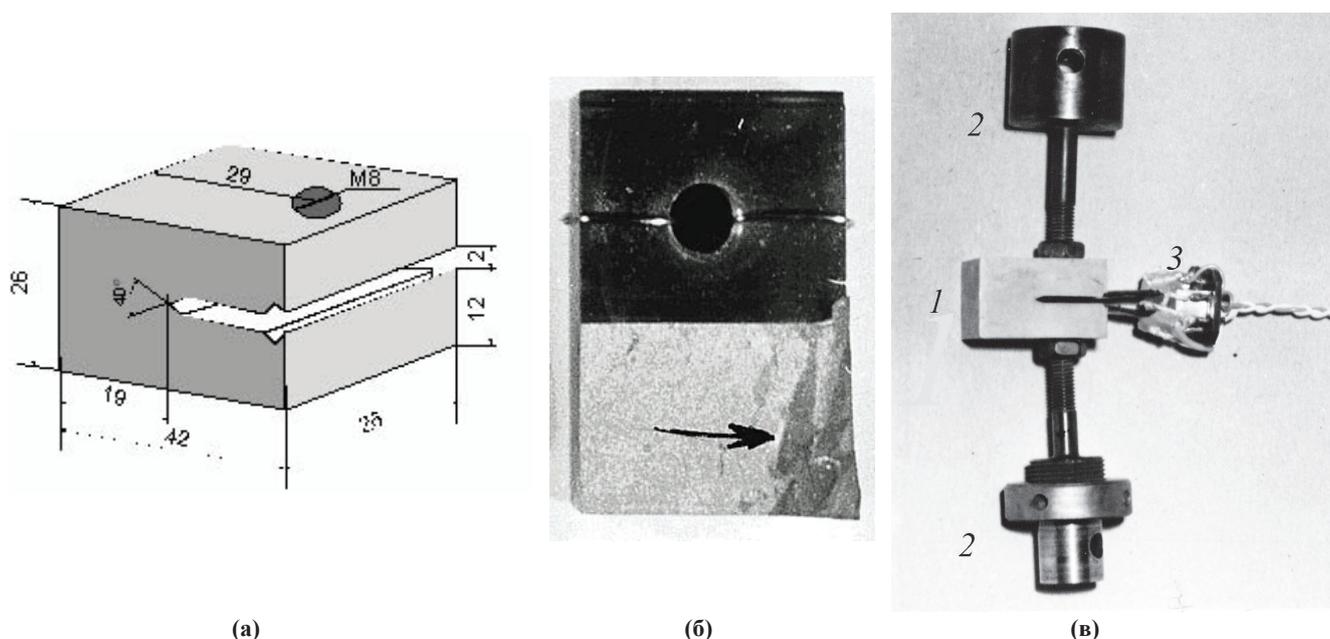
Форма, размеры образца типа WOL (а), внешний вид разрушенного образца (б), вид образца (1) с захватами (2) и датчиком раскрытия трещины (3)(в).
